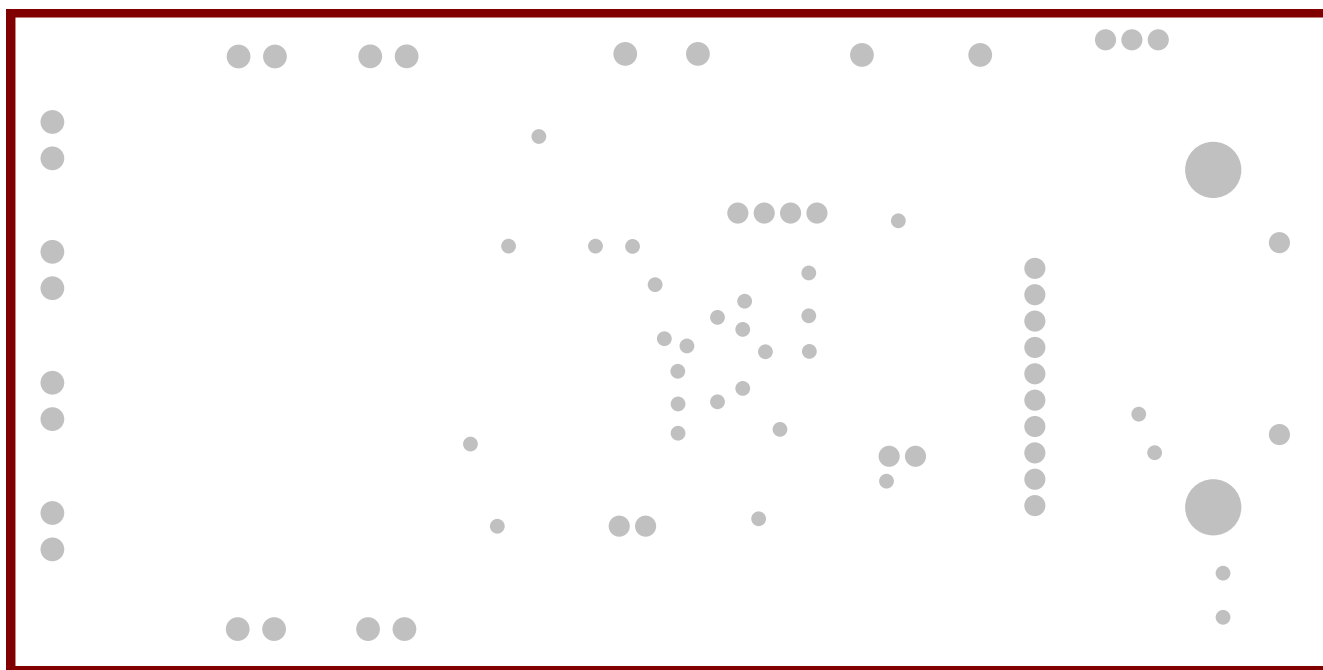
ADS131E08EVM 的 PCB 布局 (内部 AVSS/GND 平面 2)
